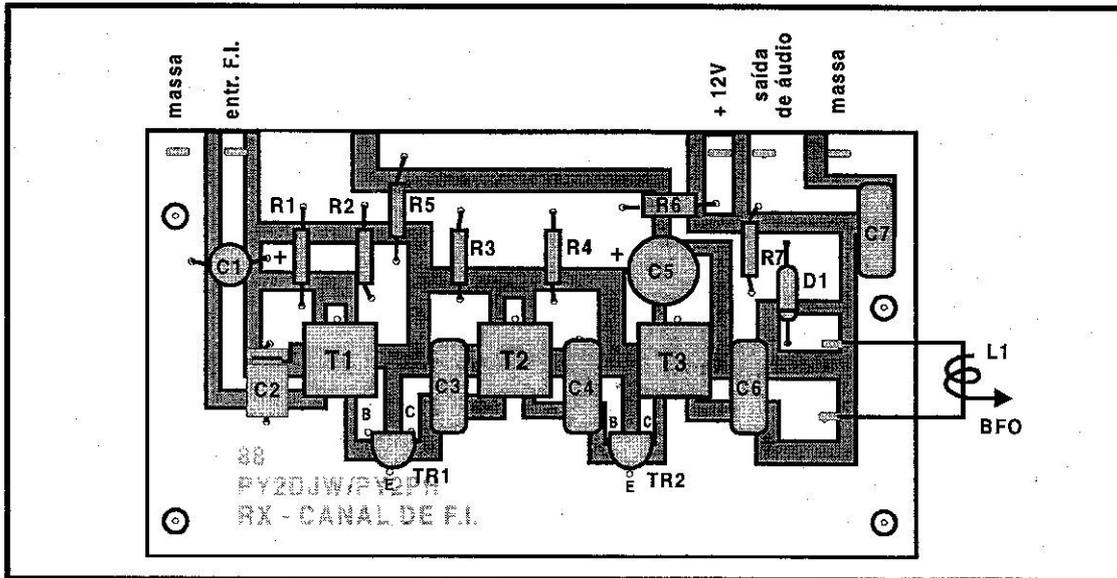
Disposição dos componentes sobre a placa de circuito impresso do canal de F.I.
